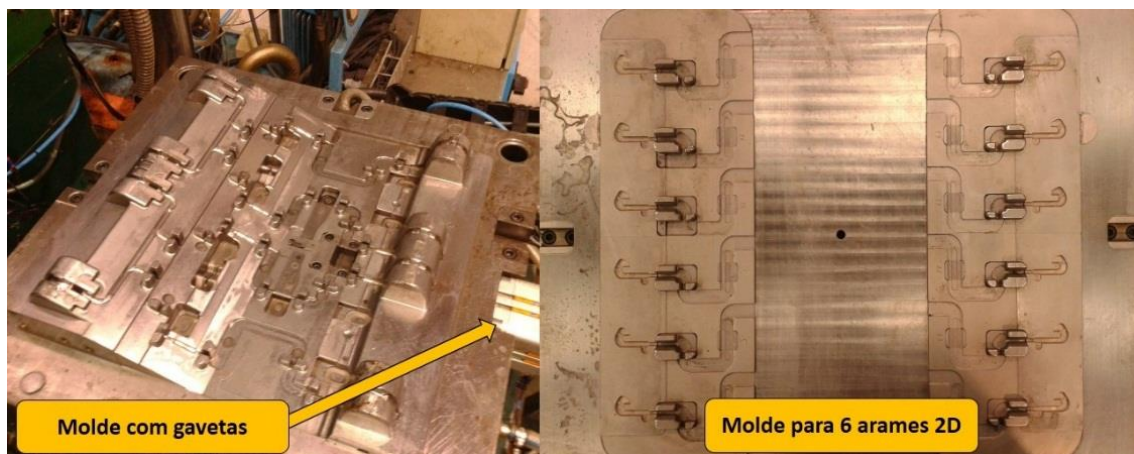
Exemplo de molde com gavetas e molde com arames 2D.
